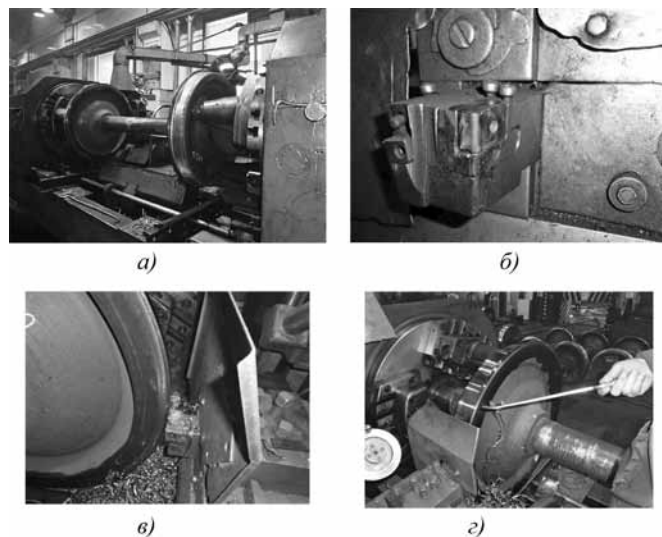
Примеры токарной обработки рабочей поверхности колес железнодорожных вагонов:
